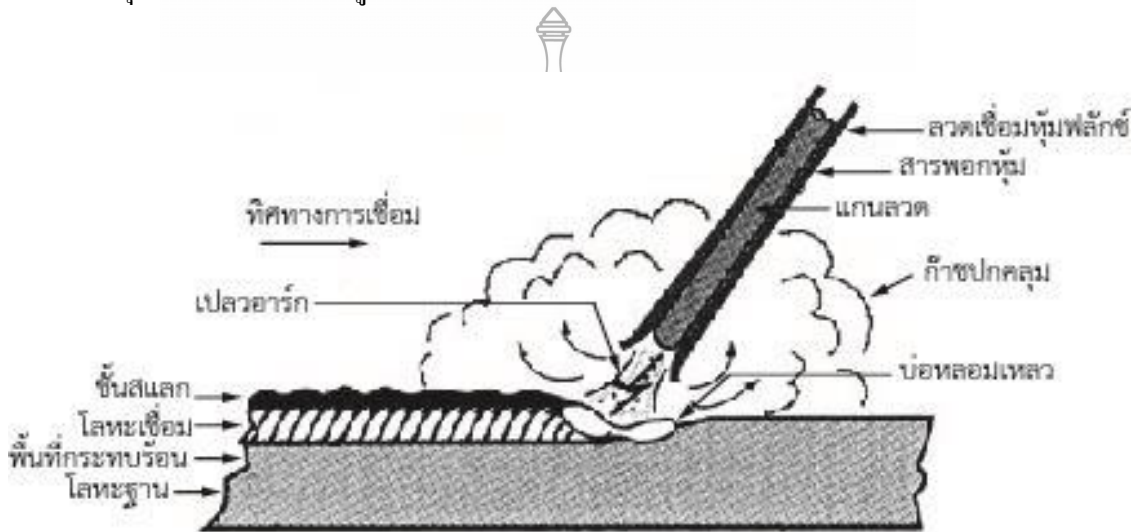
อุปกรณ์การเชื่อมอาร์กลวดเชื่อมหุ้มฟลักซ์ (Shield Metal Arc Welding; SMAW) [10]
